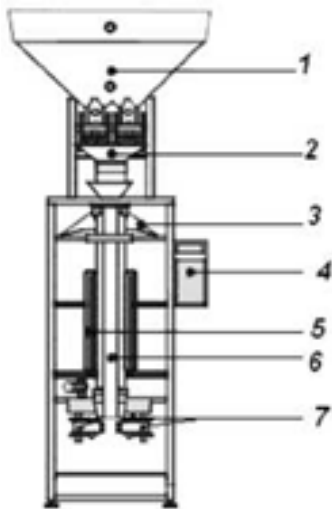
Схема вертикального фасовочно-упаковочного автомата: 1 - бункер; 2 - дозатор; 3 - воротник; 4 - пульт; 5 - система протяжки ленты; 6 - ствол; 7 - ножи, совмещённые со сварочными элементами
